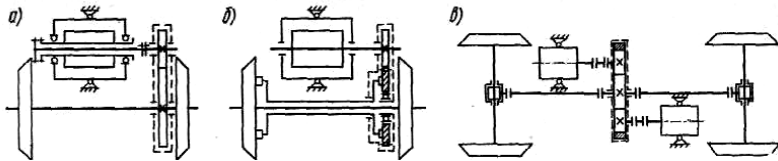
Схеми тягового приводу з карданними валами при опорно-рамному підвішуванні:
